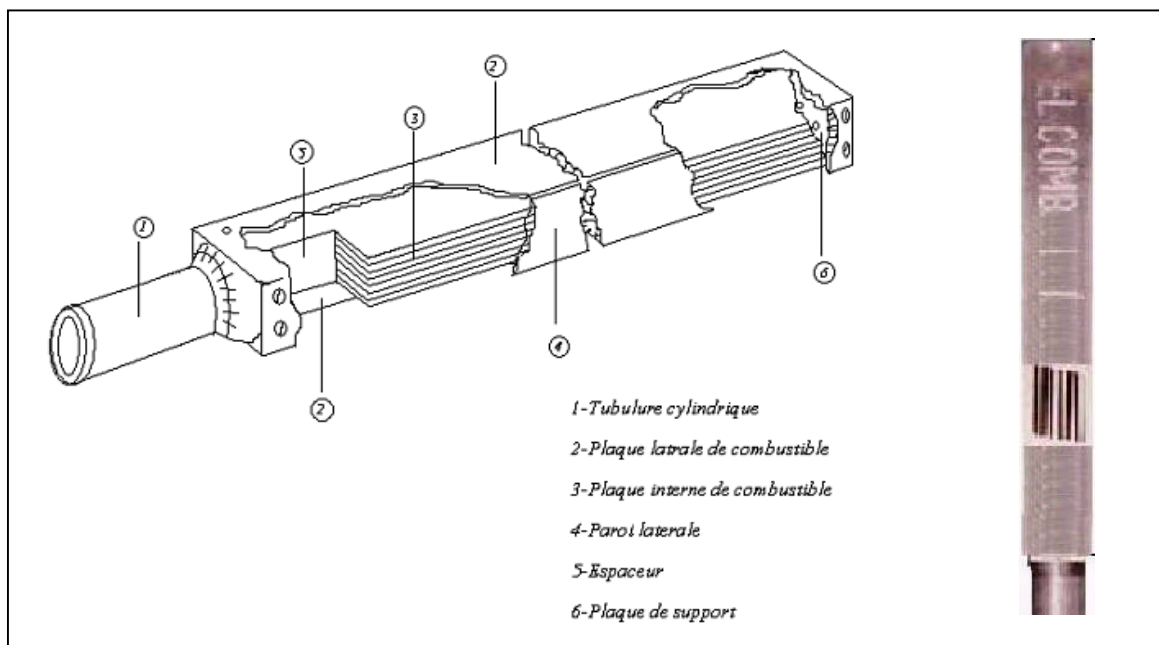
Vue d'ensemble de l'élément combustible standard.
